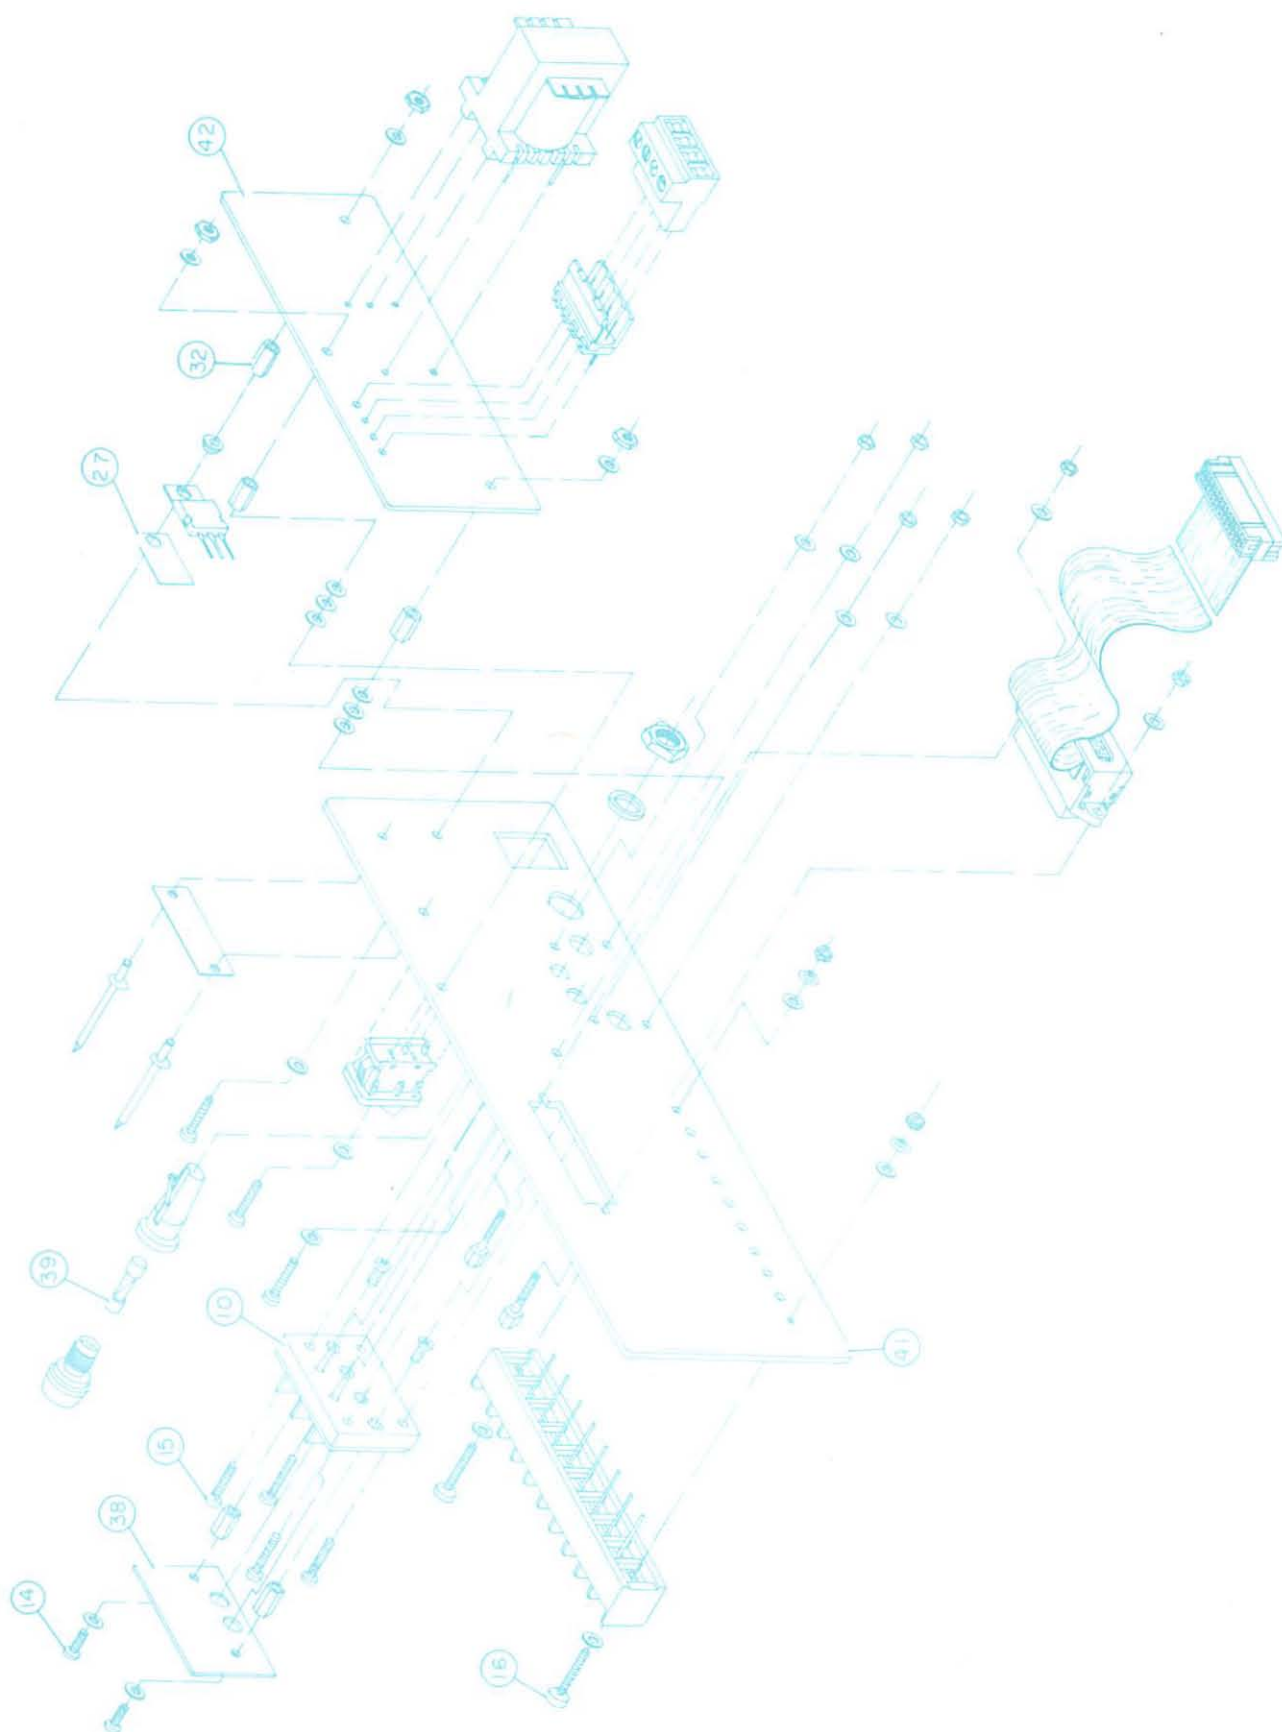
Caixa "83004004" - Montagem do painel traseiro
